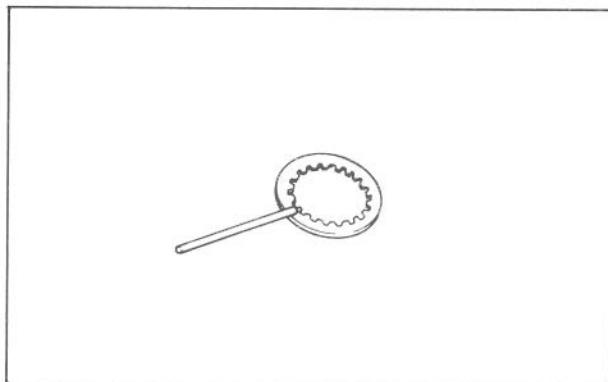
Fixador de Embreagem. Nº 90890-01022-09
